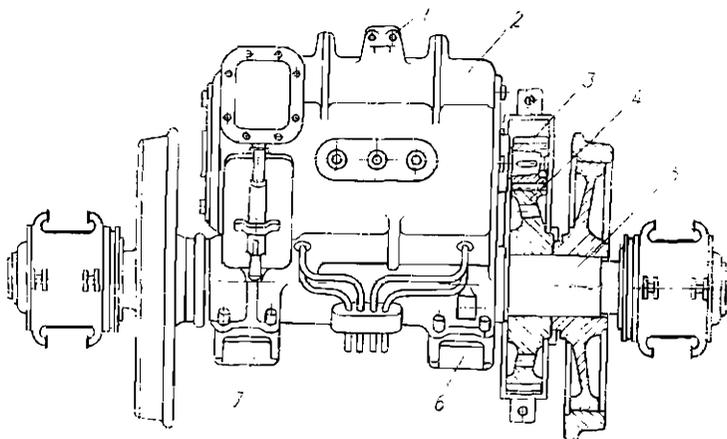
Установка тягового электродвигателя и привод колесной пары тепловоза ТЭМ2 (вид сверху).
